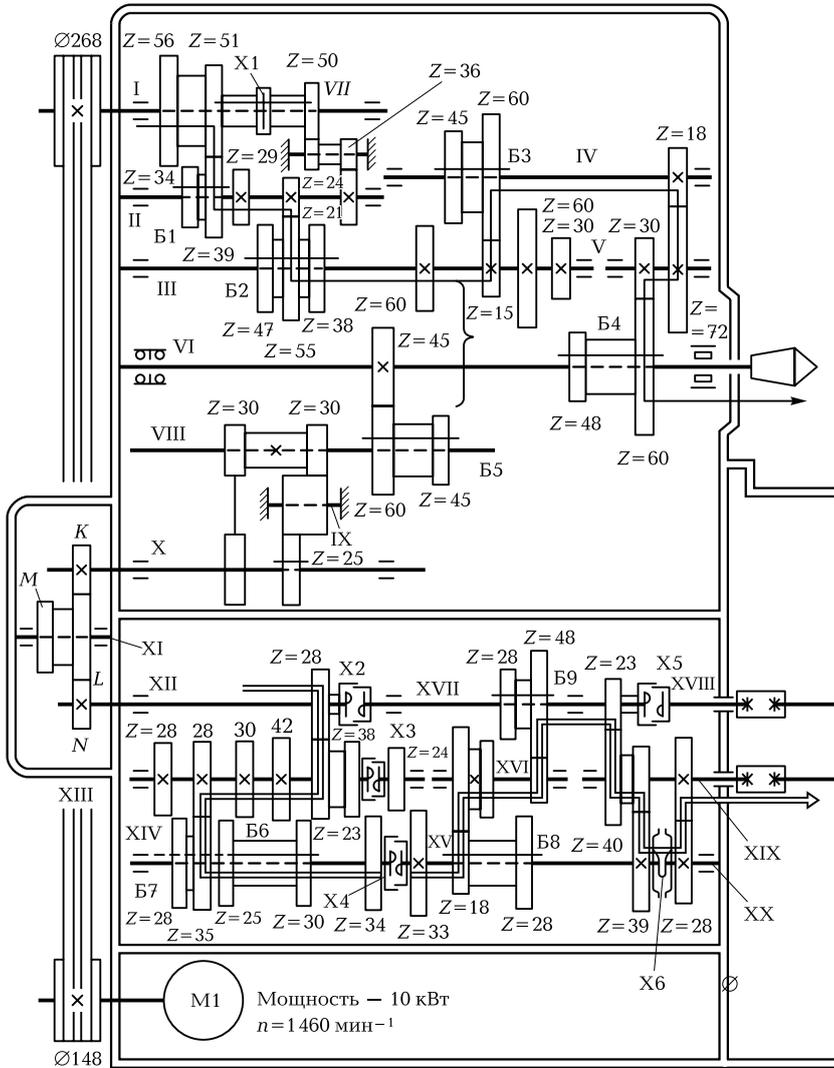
Кинематическая схема токарно-винторезного станка 16K20:
